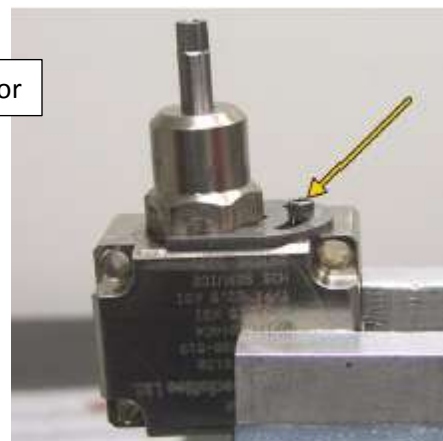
Instalación O-ring 2-205 V75 de Pre-ensamblaje Bonnet en la válvula.
